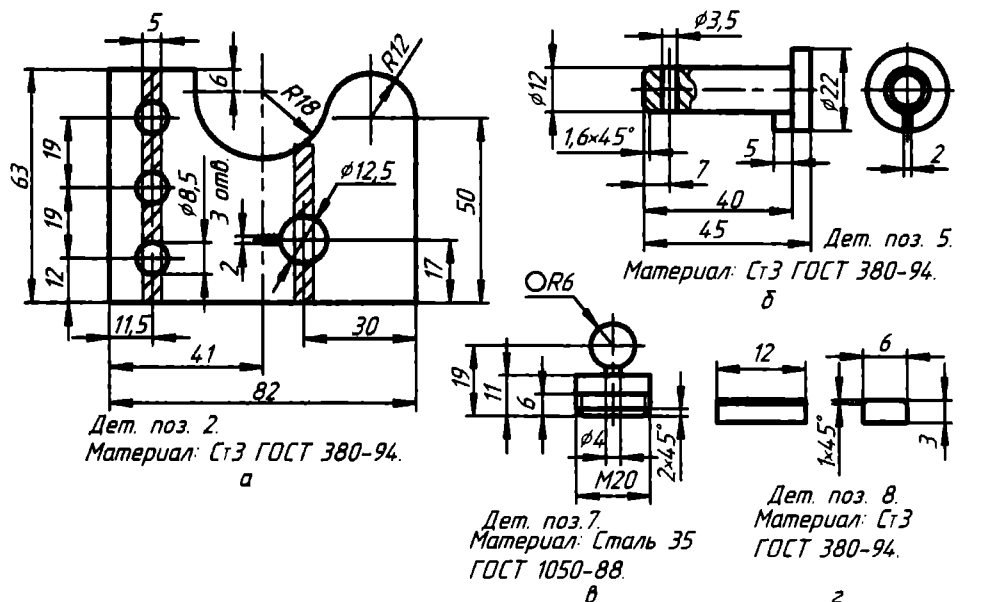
Чертежи: а — щеки; б — оси; в — пробки; г — шпонки
